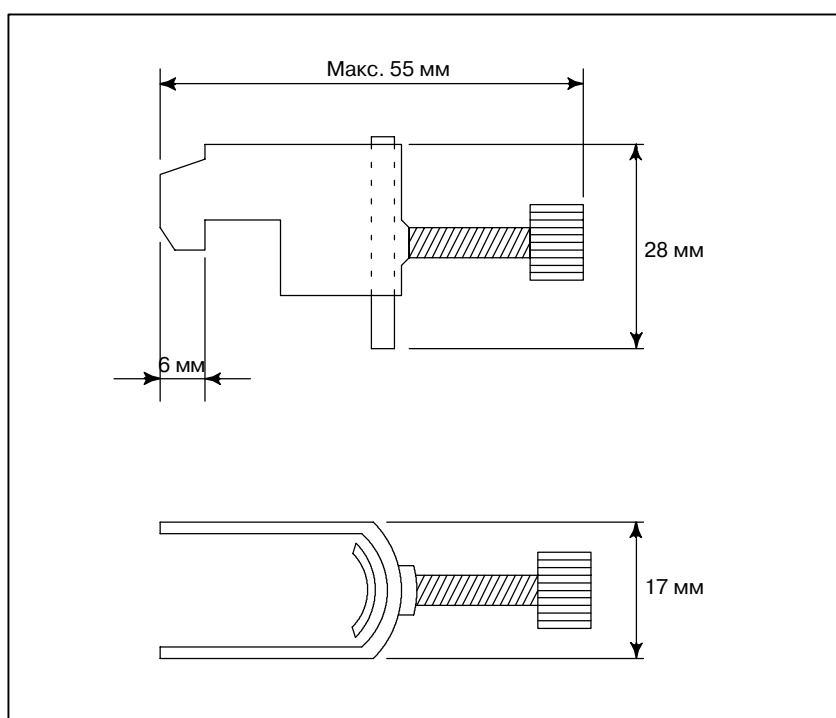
(e) Габаритные чертежи металлической арматуры для крепления
